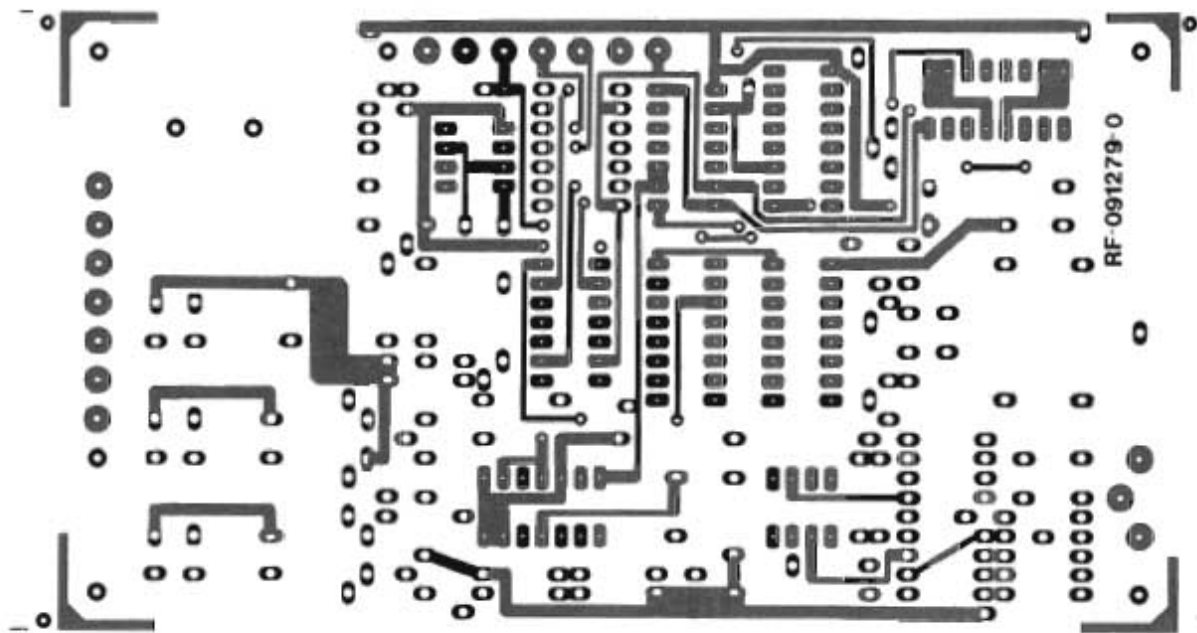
Master, lato componenti, in scala 1:1, del circuito stampato della basetta principale.
